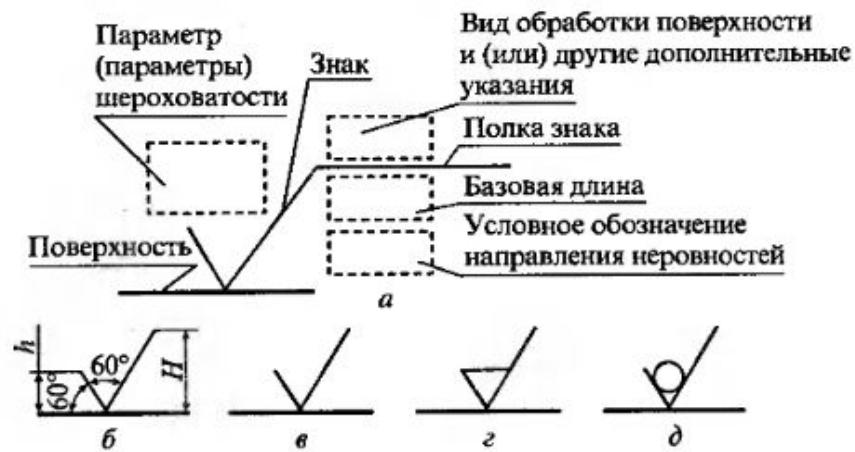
Структура и знаки обозначения шероховатости поверхности:
